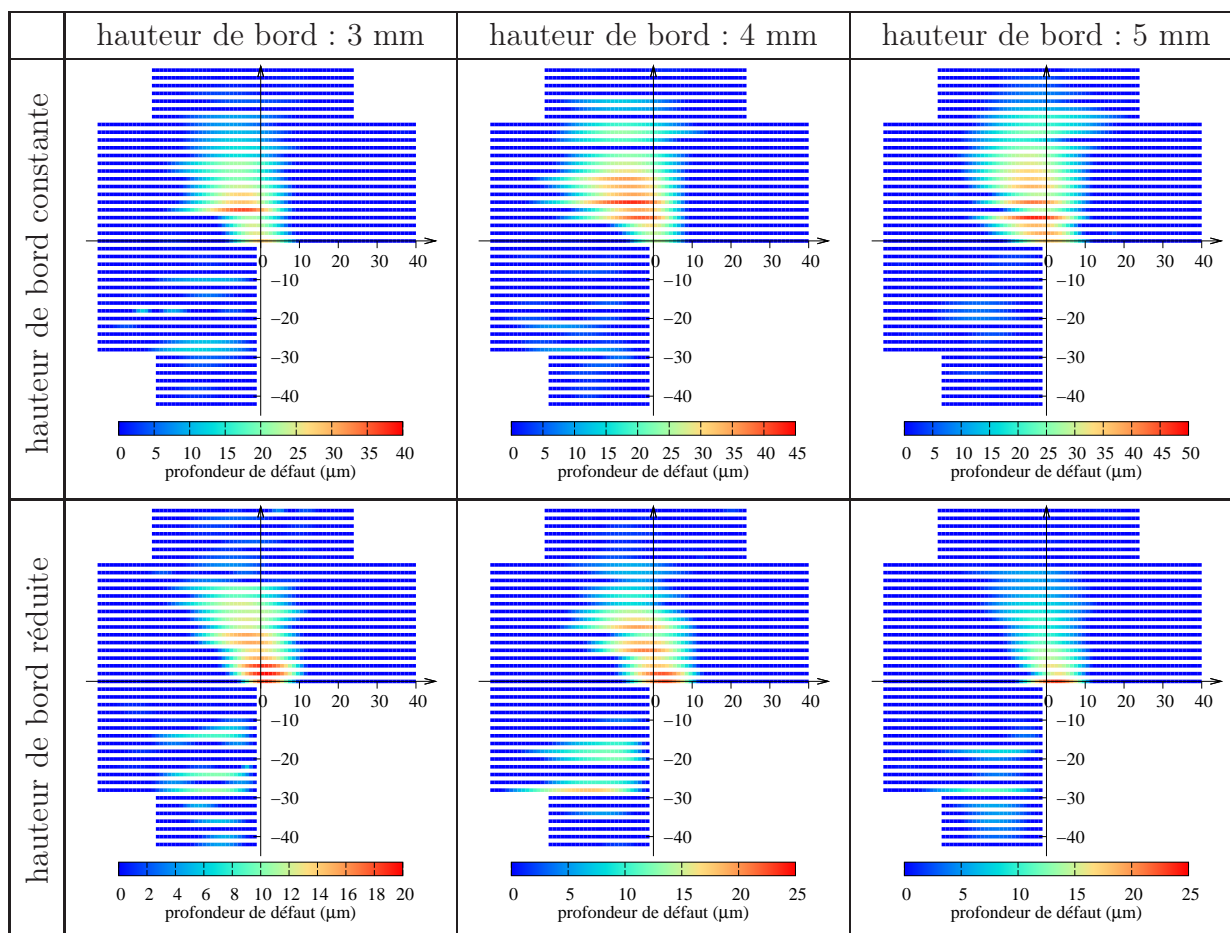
Cartographie des profondeurs de défaut des éprouvettes en DP500 pour plusieurs hauteurs de bord
